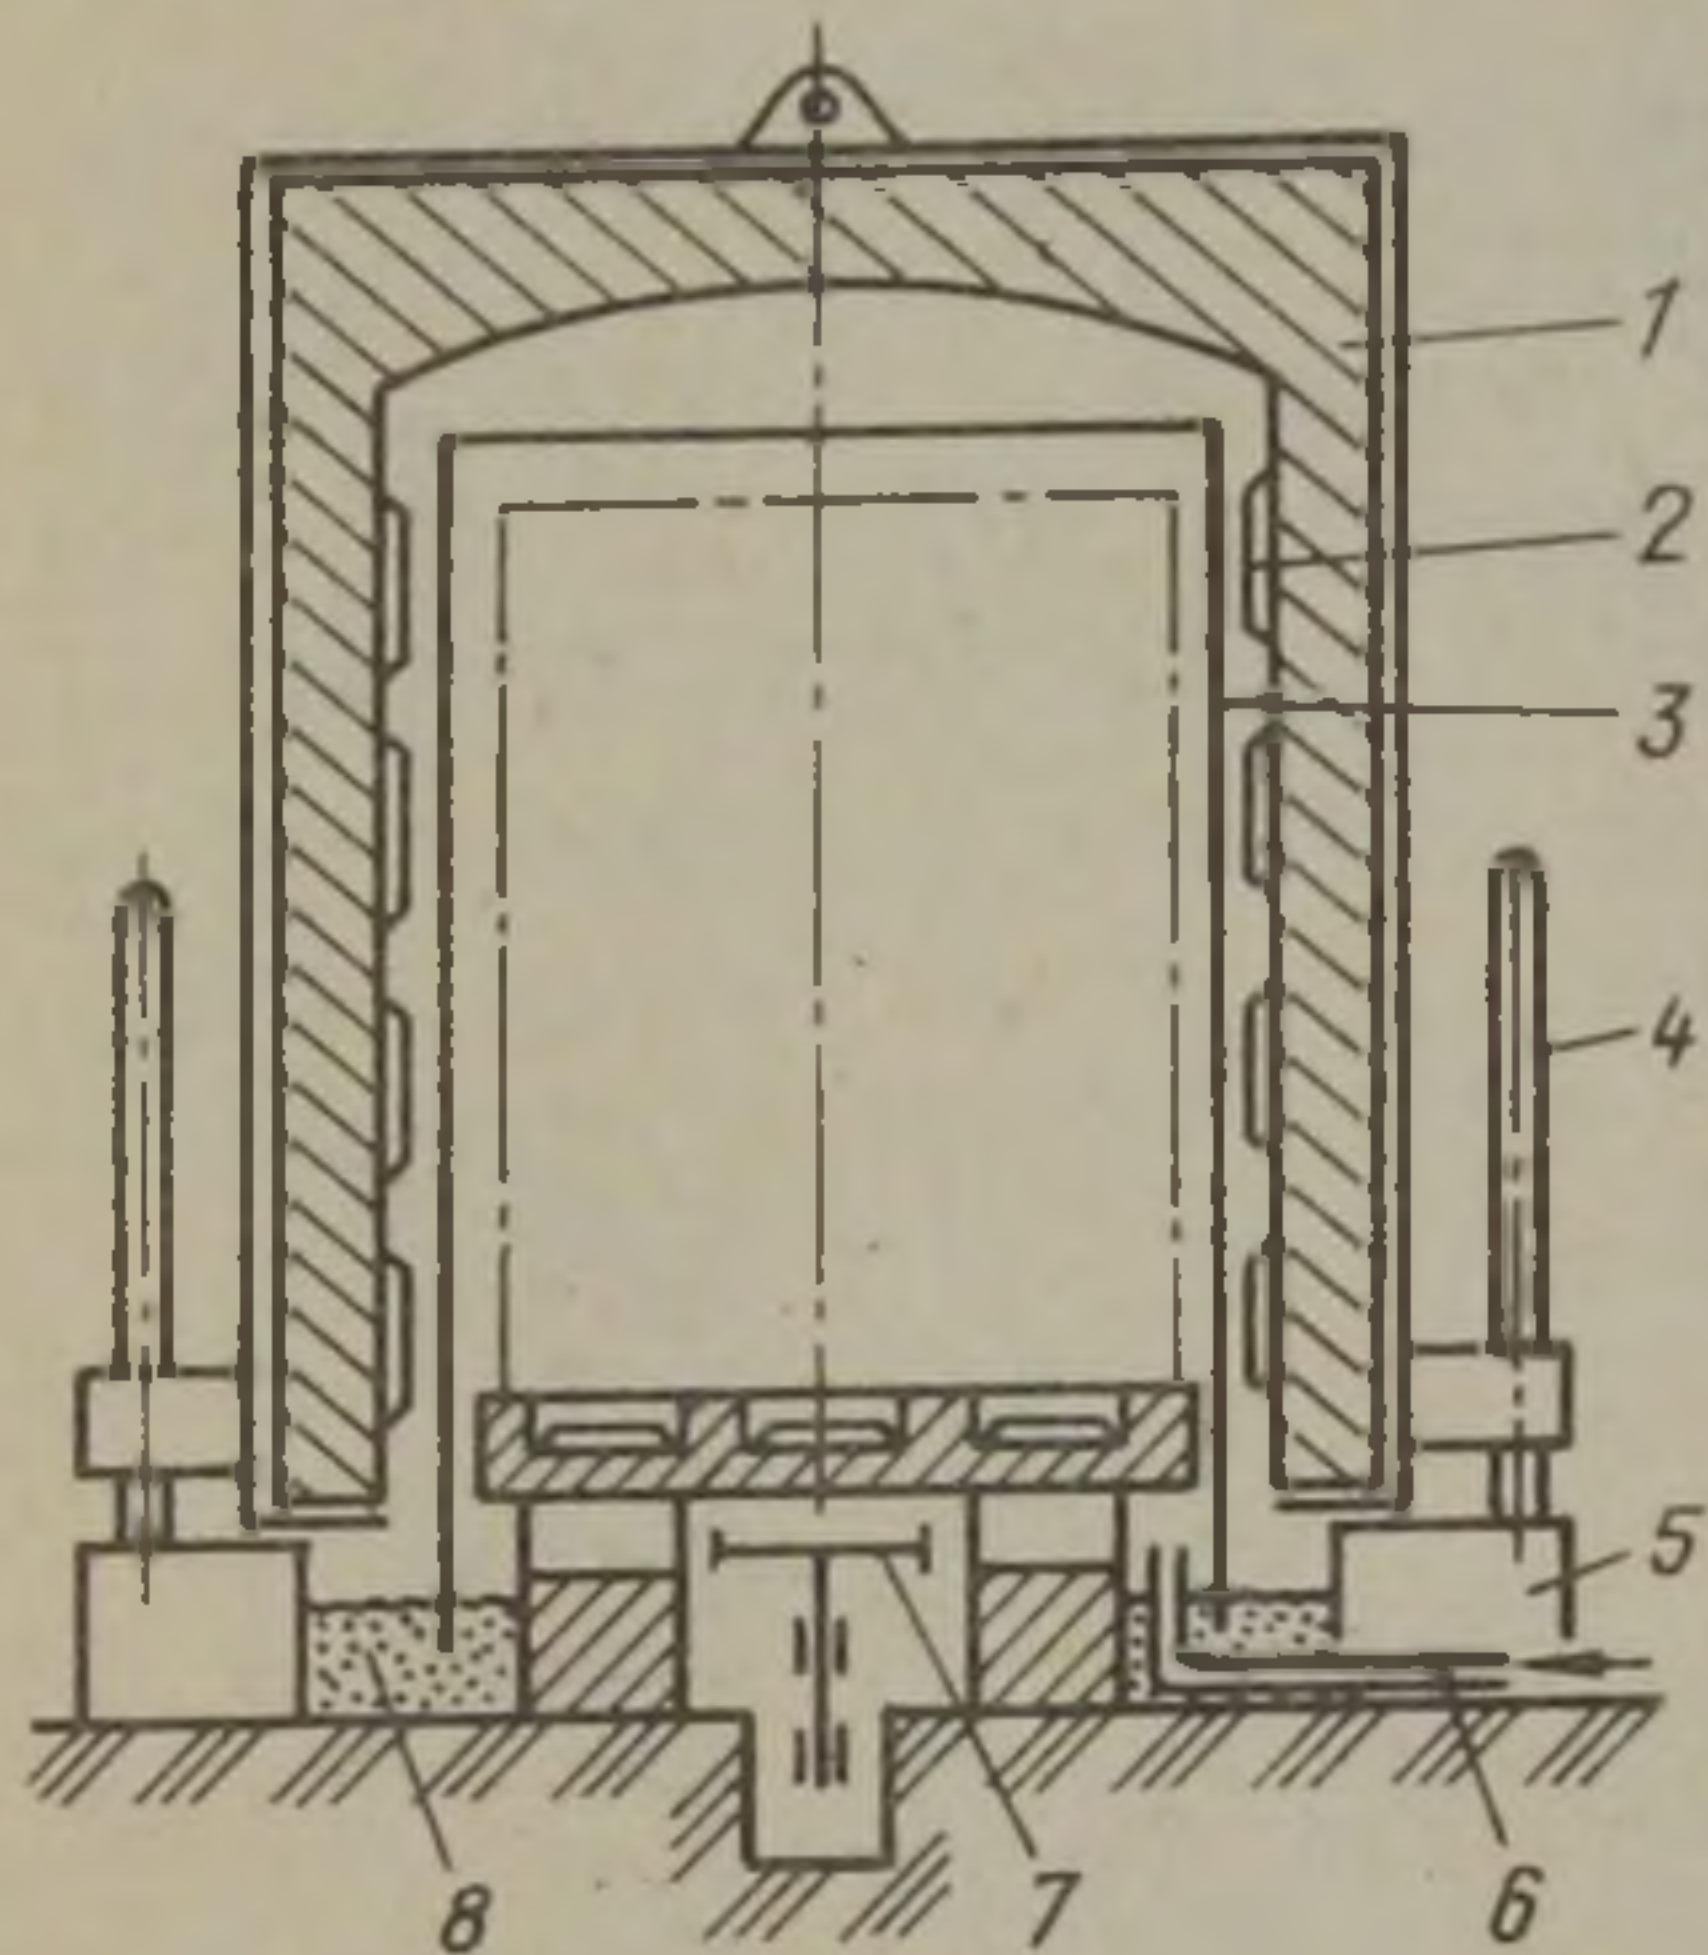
Схема колпаковой печи типа СГЗ:
